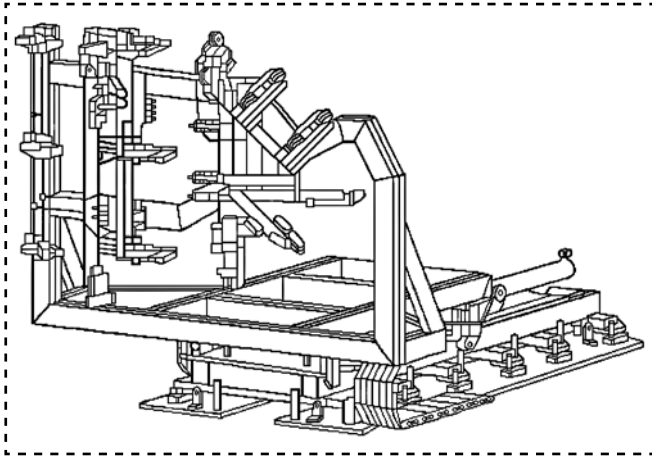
Подвижный сварочный кондуктор (каретка) с узлами фиксации боковин на операциях сварки кабин автомобилей семейства "ГАЗелей"
